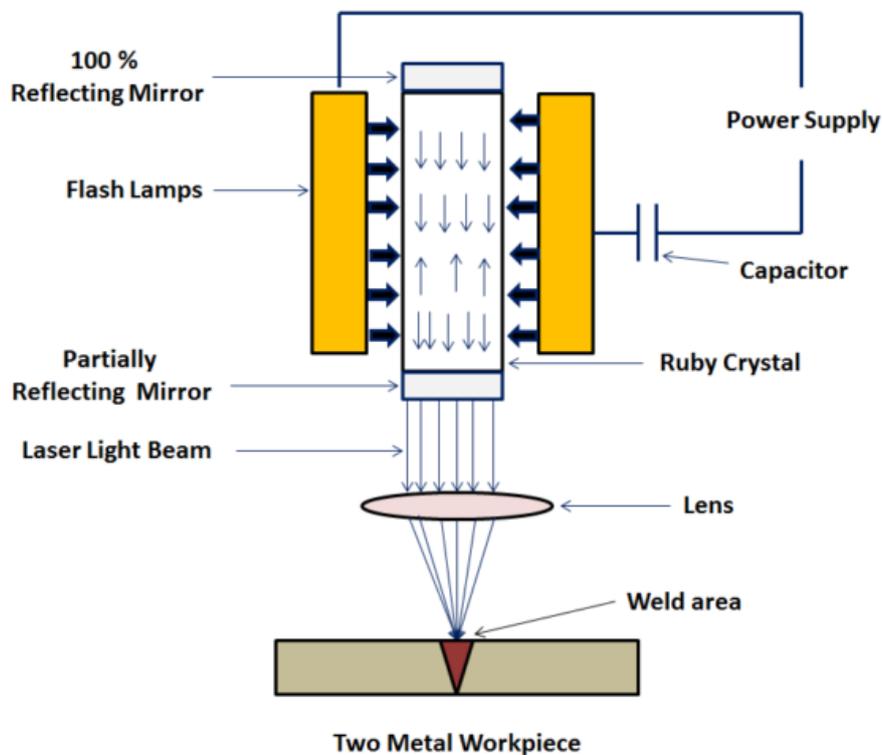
Esquema de soldadura LBW (Fuente: theweldingmaster.com)
